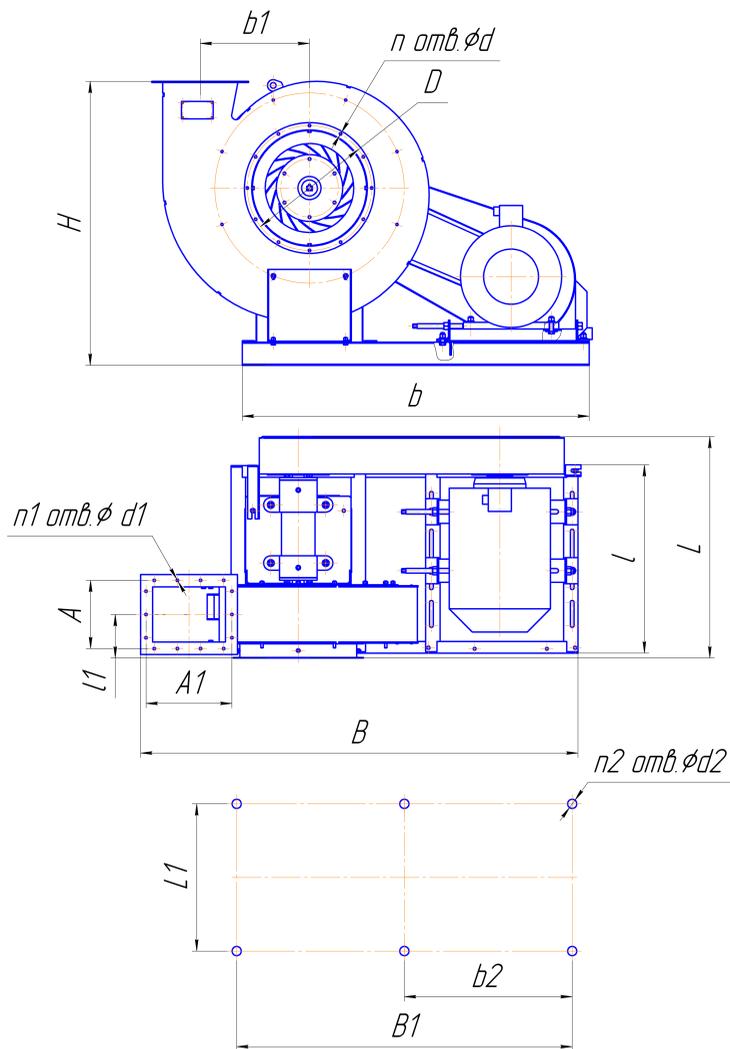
Габаритные, присоединительные и установочные размеры вентиляторов ВР132-30-(5-10).
